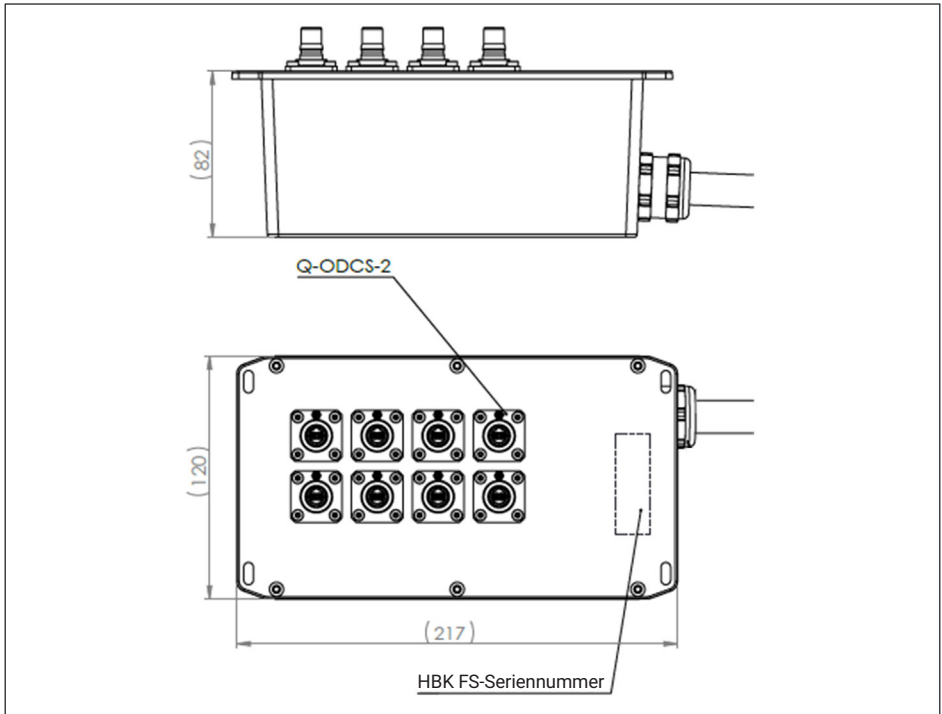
Anschlussbox – Boxseite – technische Zeichnung (Abmessungen in mm)
